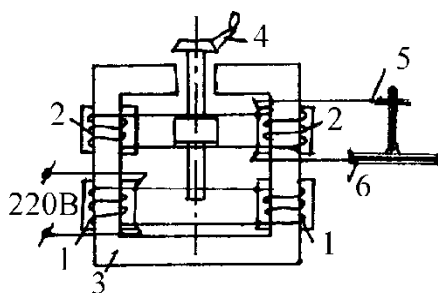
Принцип работы сварочного трансформатора
